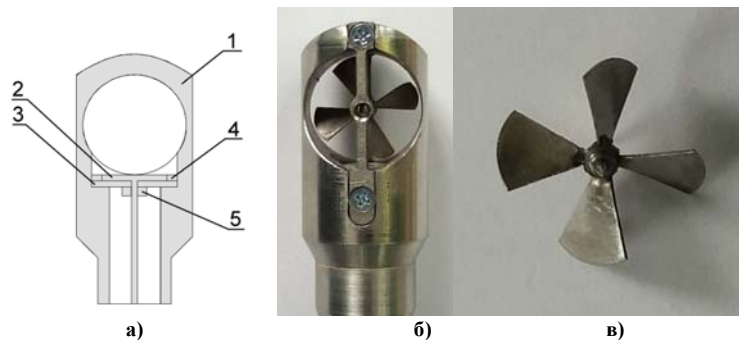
а) поперечний переріз голівки. 1 – корпус, 2 – обкладка базової ємності, 3 – слюдяний діелектрик, 4 – герметик, 5 – гайка, б) голівка в сборі, в) крильчатка
